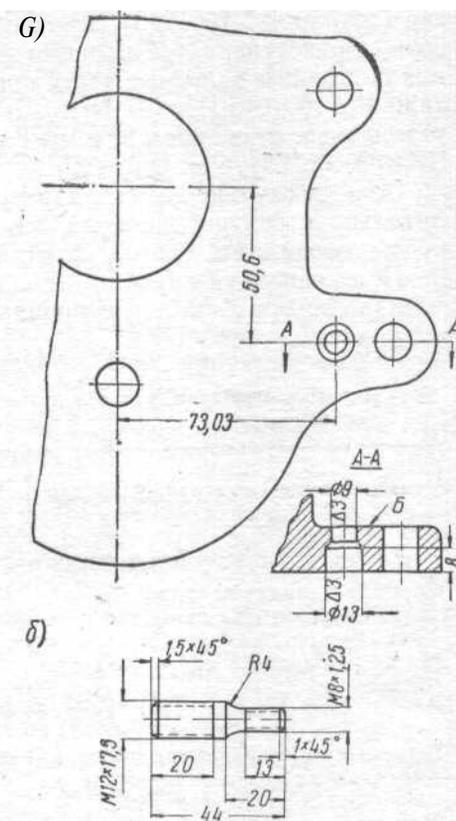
Подготовка картера коробки передач модели 407 при ее установке взамен коробки передач модели 402: а — координаты дополнительного отверстия в лапе картера; б — переходная шпилька крепления картера коробки передач к картеру сцепления
